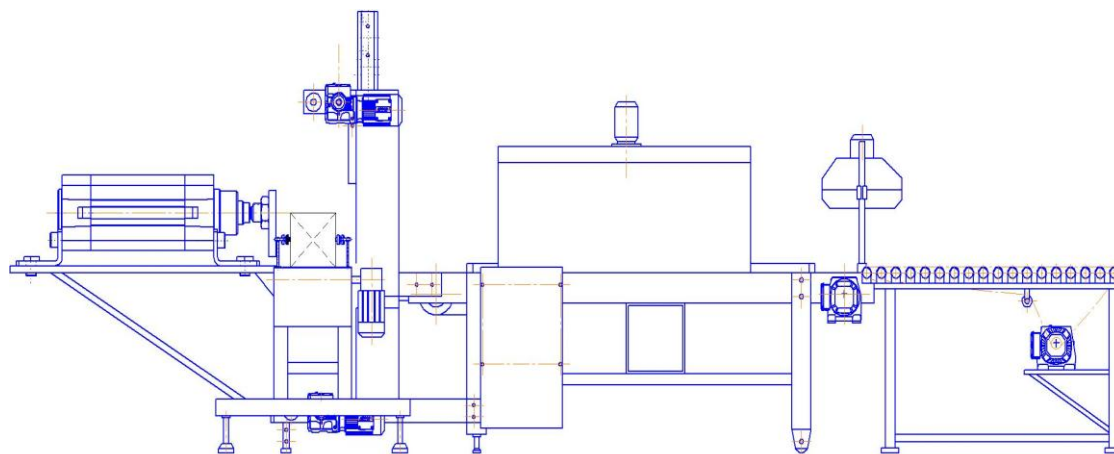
Машини для формування групової упаковки з жестианих банок
